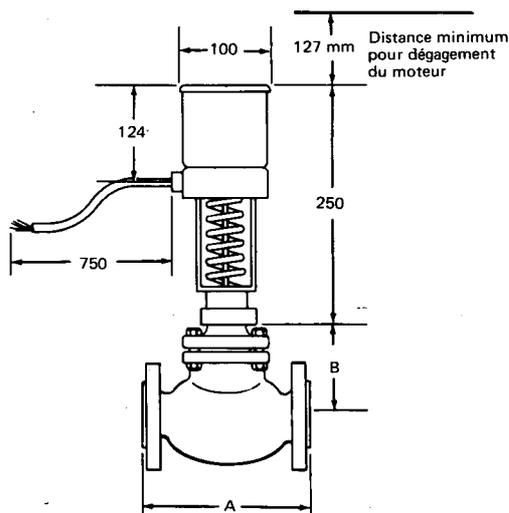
Dimensions en mm avec moteur électro-hydraulique
